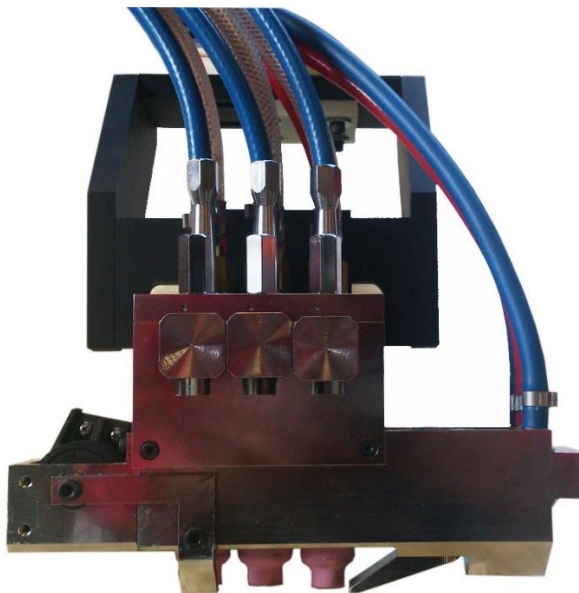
Sistema de soldagem que utiliza 3 tochas TIG em sequência, utilizado para fabricação de tubos com costura. Fonte: www.ledica.it [18]
